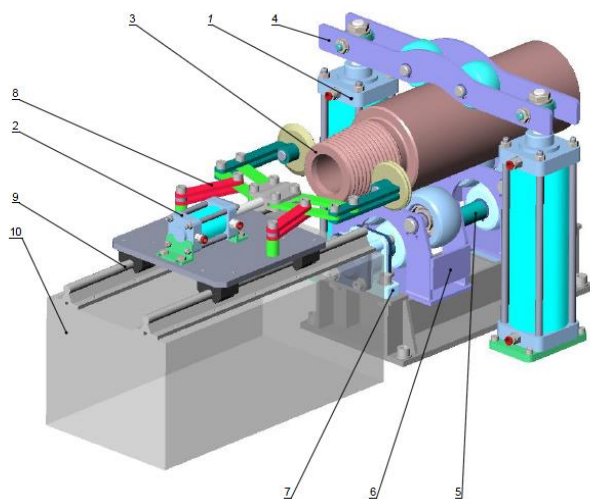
Установка для электромеханической поверхностной закалки наружной резьбы бурильной трубы.
